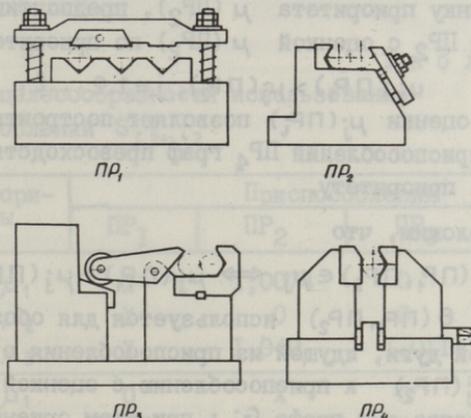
Технически приемлемые приспособления для операции фрезерования торца валика: $PP_1 \dots PP_4$ - обозначения приспособлений.
